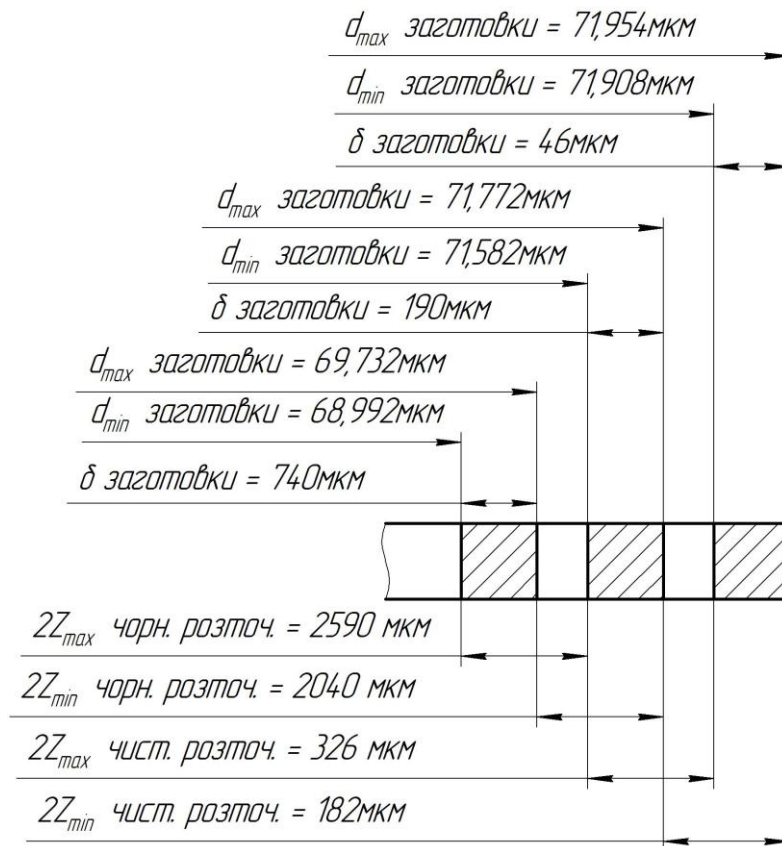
Схема графічного розміщення припусків і допусків на обробку отвора корпусу
